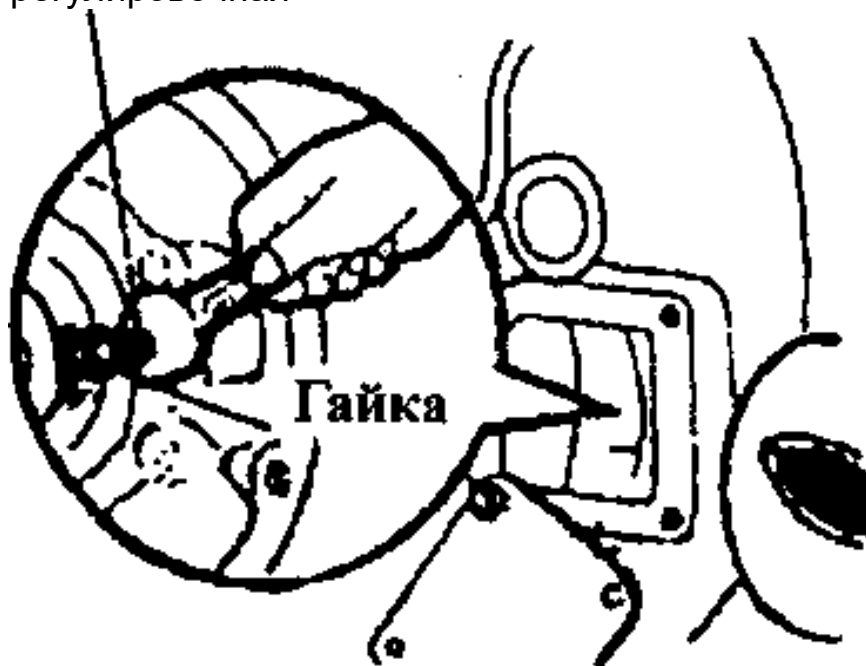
Регулировка зазора между отжимным кольцом и выжимным подшипником
